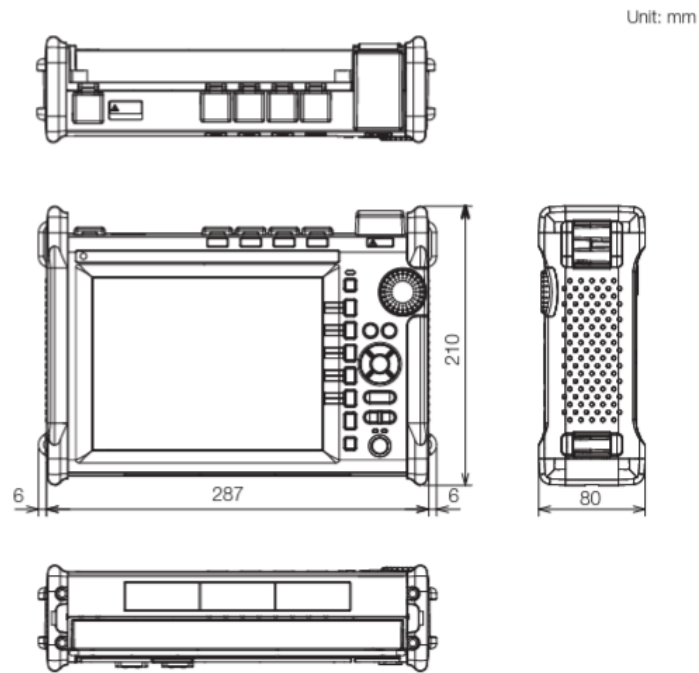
Dimensiones del AQ7280. Fuente: [19].
